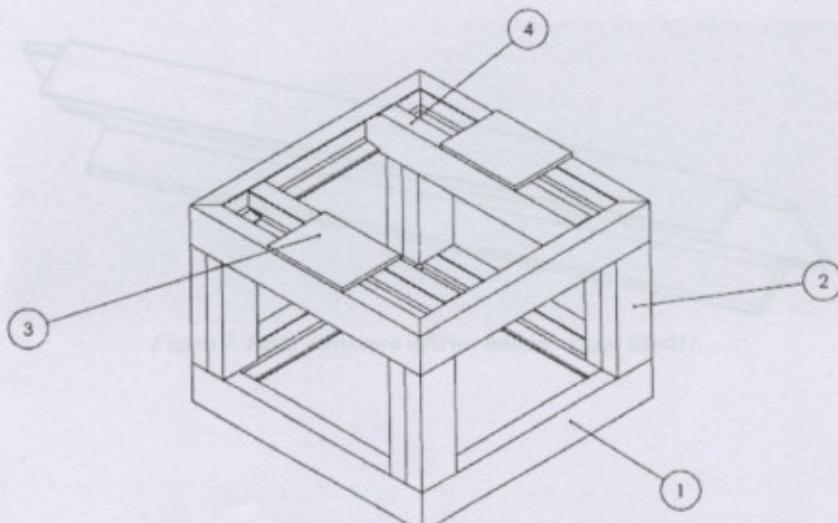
Ensamblaje estructura inferior. Plano E-E-I
